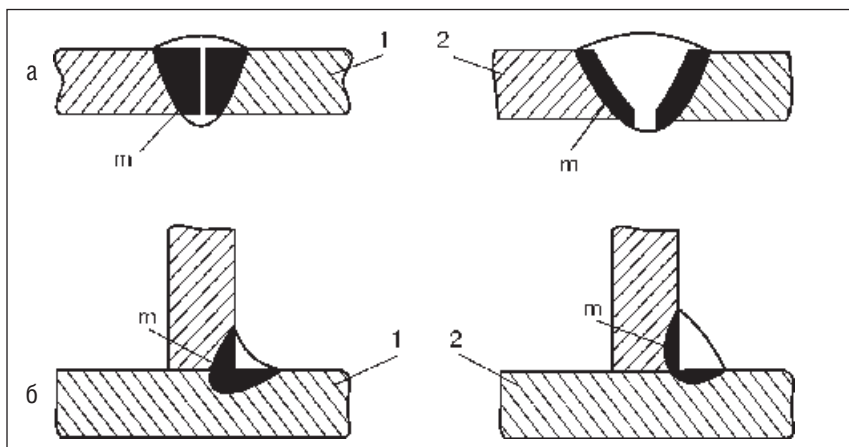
Доля участия основного металла m в формировании металла шва при сварке среднеуглеродистых сталей: а — в стыковом шве; б — в угловом шве (1 — шов с большой долей участия; 2 — то же, с малой)
